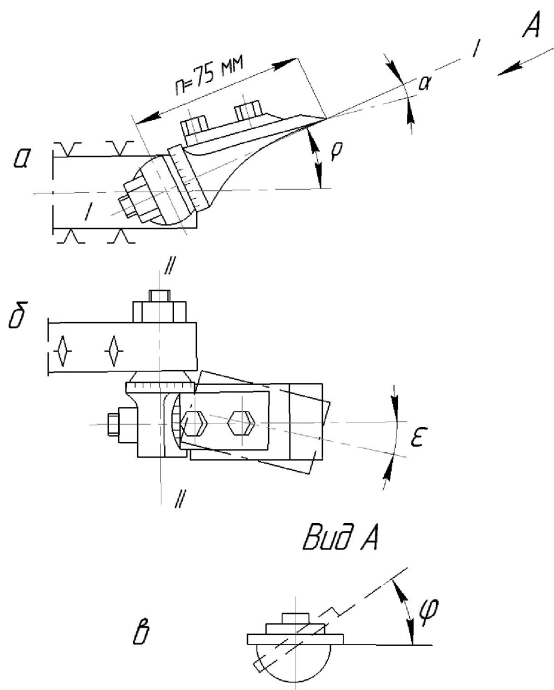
Конструкция узла резания с черновым резцом для оцилиндровки бревен:
